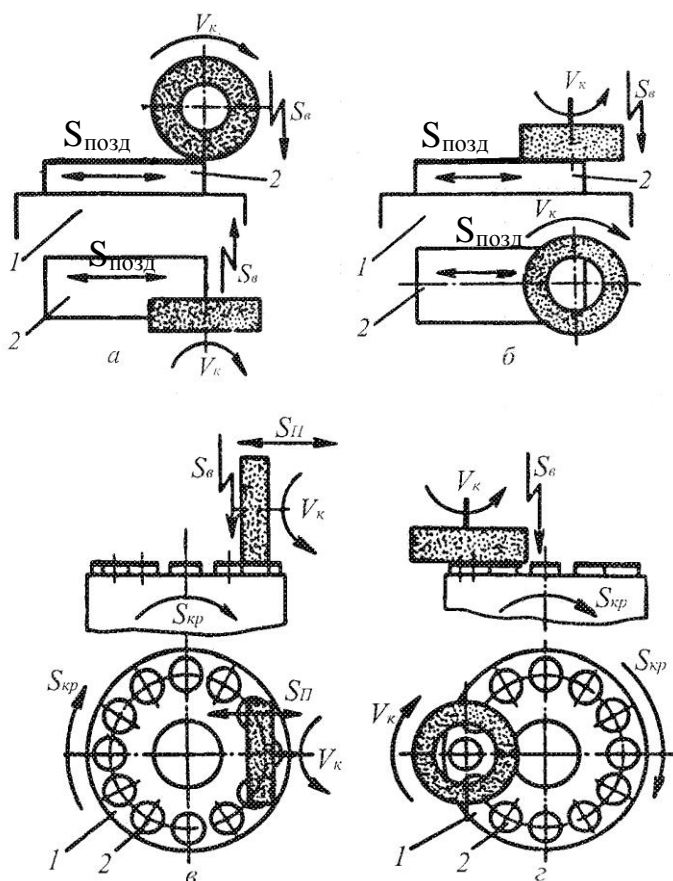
Схеми обробки заготовок на плоскошліфувальних верстатах
